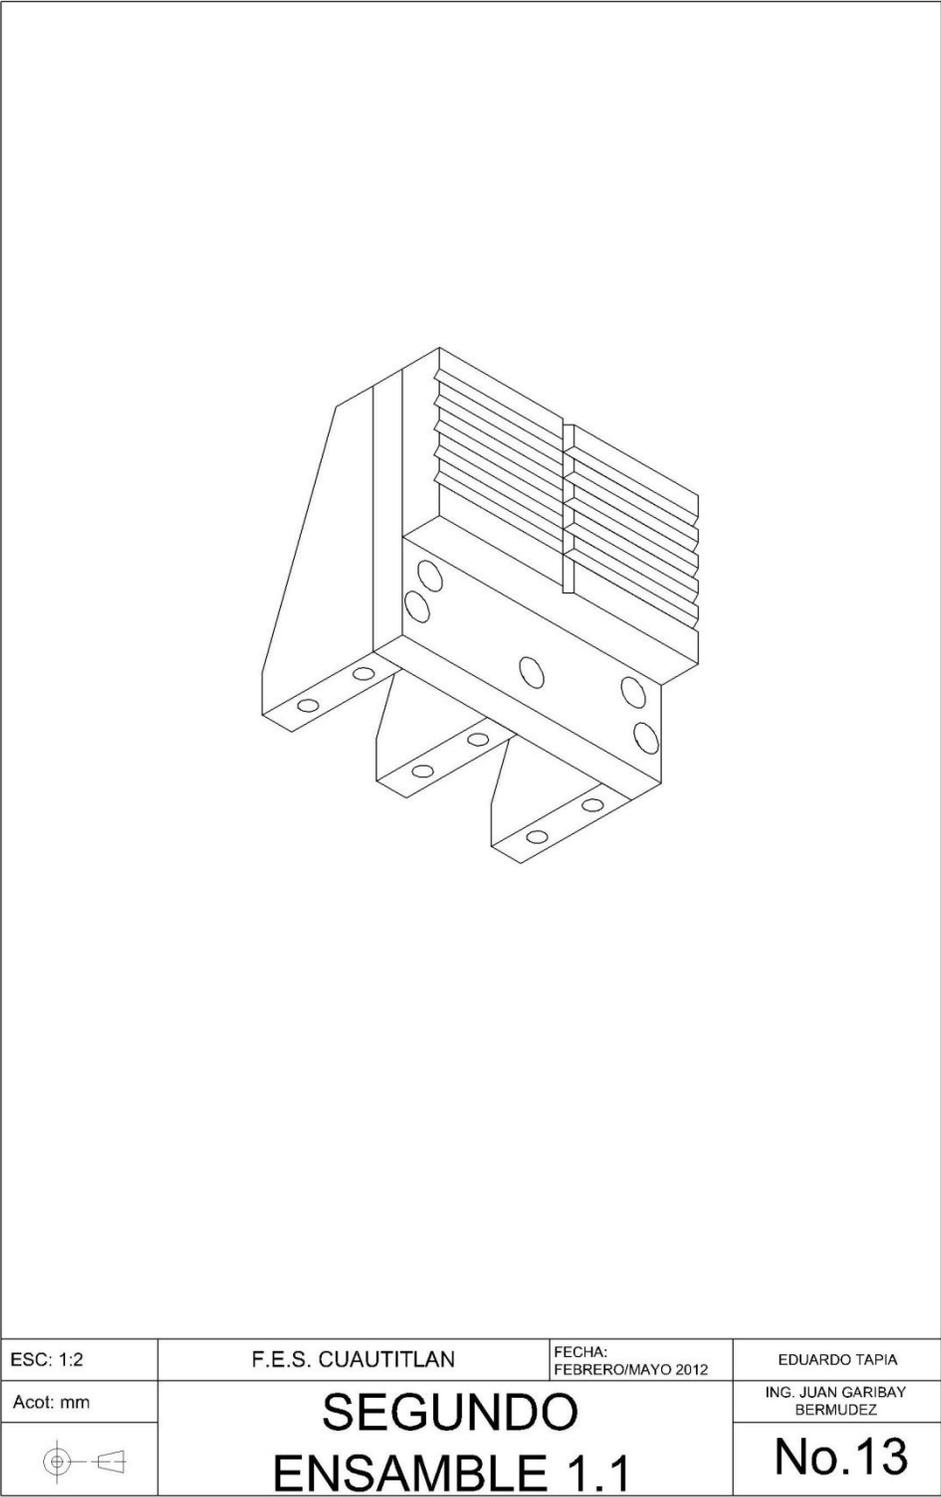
Vista en isométrico de la construcción del cabezal fijo secundario.
